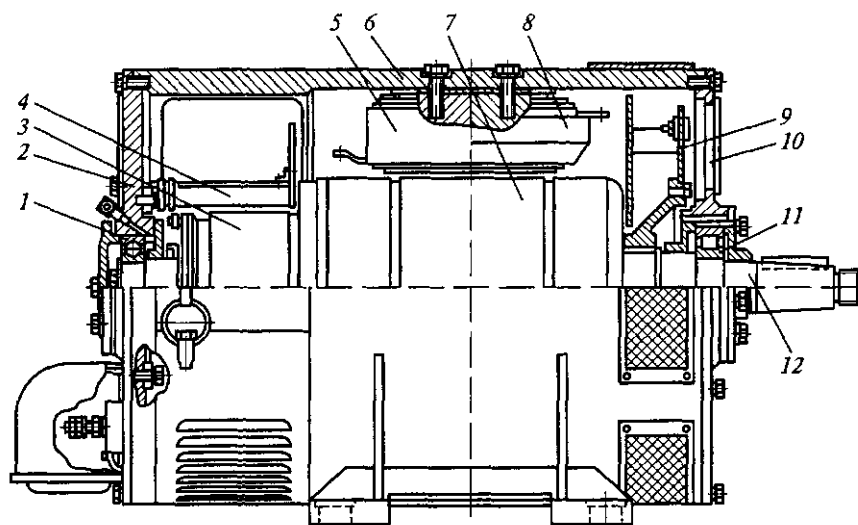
Схема стартер-генератора: 1,11-підшипники; 2,10-передній і задній підшипникові кришки щити; 3-колектор; 4-траверс; 5-головний полюс; 7-якір; 8-додатковий полюс; 9-вентелятор; 12-вал.
